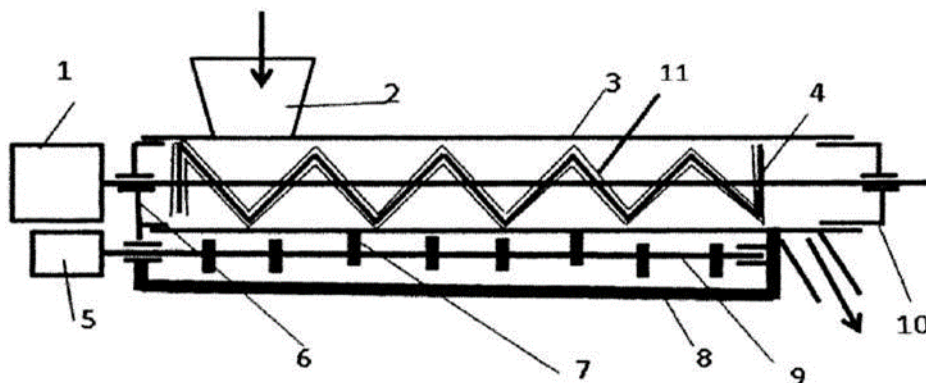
Спосіб передпосівної обробки насіння та пристрій для його здійснення: 1 – привод шнека; 2 – бункер; 3 – камера обробки; 4 – шнек; 5 – привод спонукача; 6 – опора; 7 – циліндричні кулачки; 8 – рама; 9 – вал спонукача; 10 – опора; 11 – чохол
